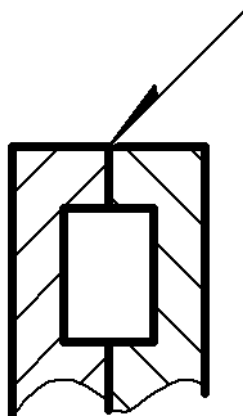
Конструкция сварного соединения для удаления окисной пленки из зоны соединения
